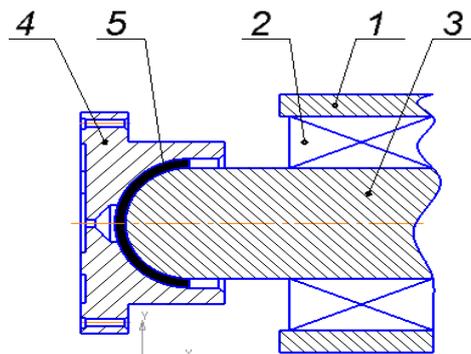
Схема обработки внутренней сферической поверхности подпятника:
